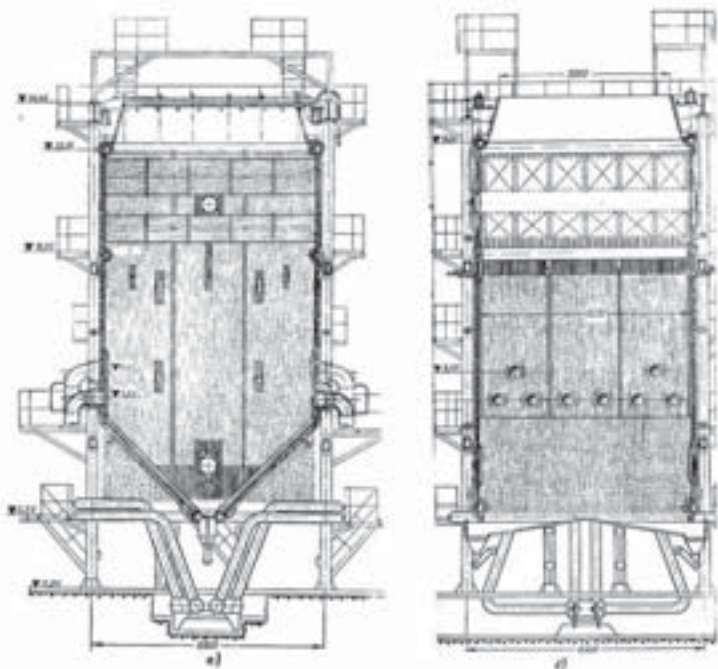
Общий вид котла башенного типа ПТВМ-100 (а – продольный разрез; б – поперечный разрез)
